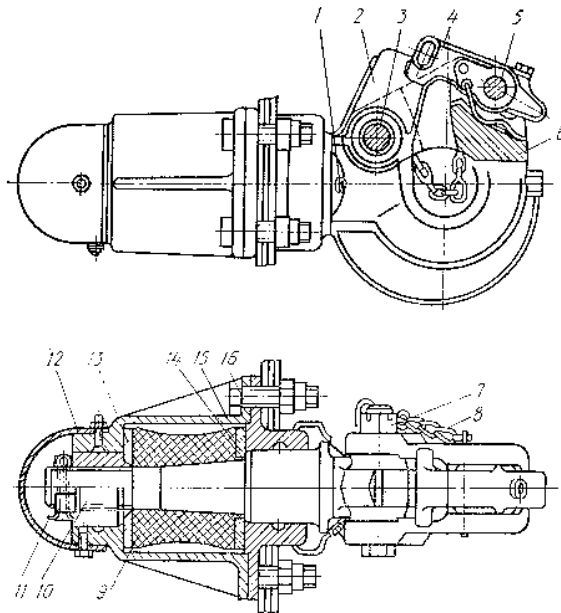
Тягово-зчіпний пристрій автомобіля тягача КамАЗ-5320: 1 – маслянка; 2 – гак; 3 – вісь засувки гака; 4 - собачка засувки; 5 – вісь собачки; 6 - клямка; 7 – гайка; 8 – ланцюжок шплінту; 9 – пружний елемент; 10 – гайка гака; 11 – шплінт; 12 – захисний кожух; 13, 14 - шайби; 15 – корпус; 16 – кришка корпусу
